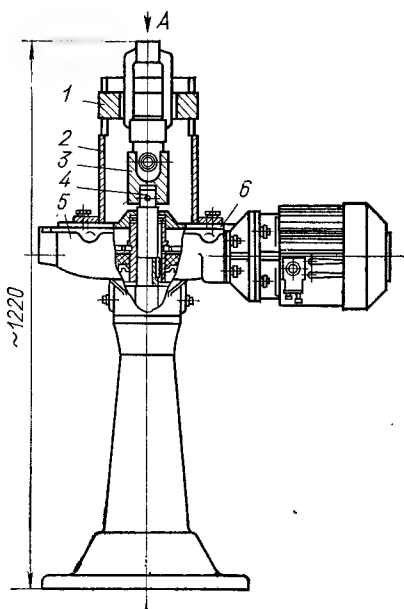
Станок для свинчивания бугеля с корпуса вентиля:
